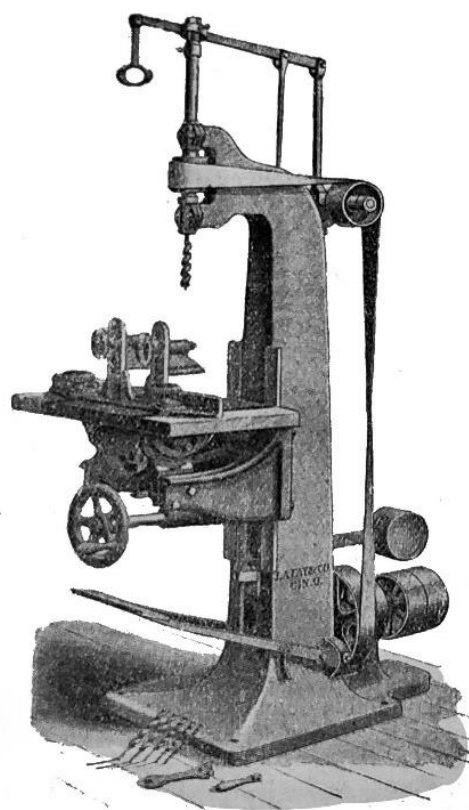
Máquina vertical de furar. Ilustração de COLARES, 19--: 260.
